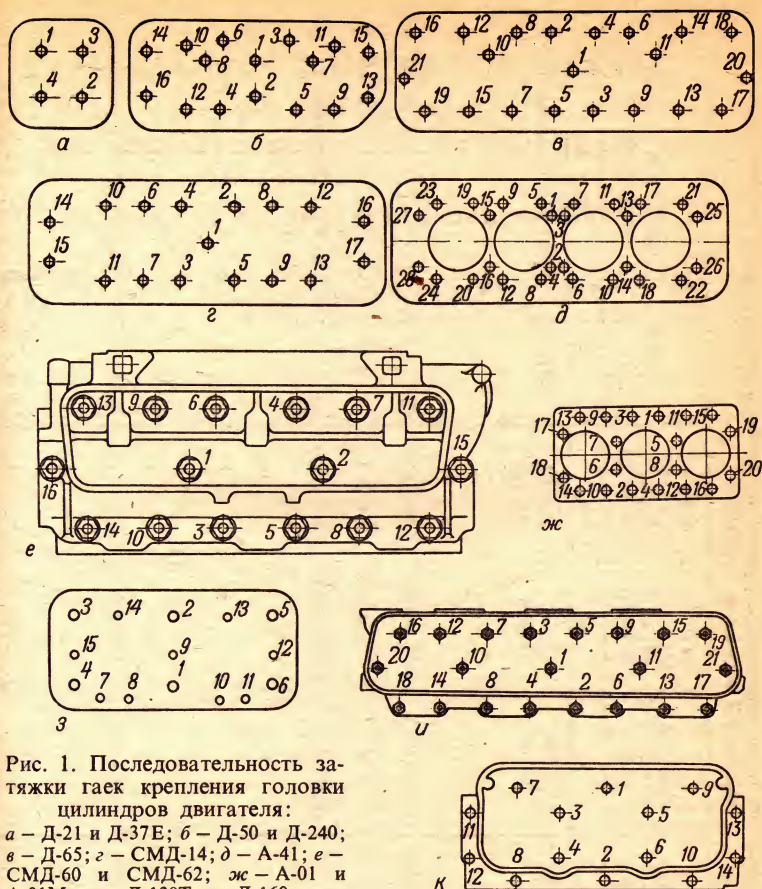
Последовательность затяжки гаек крепления головки цилиндров двигателя:
